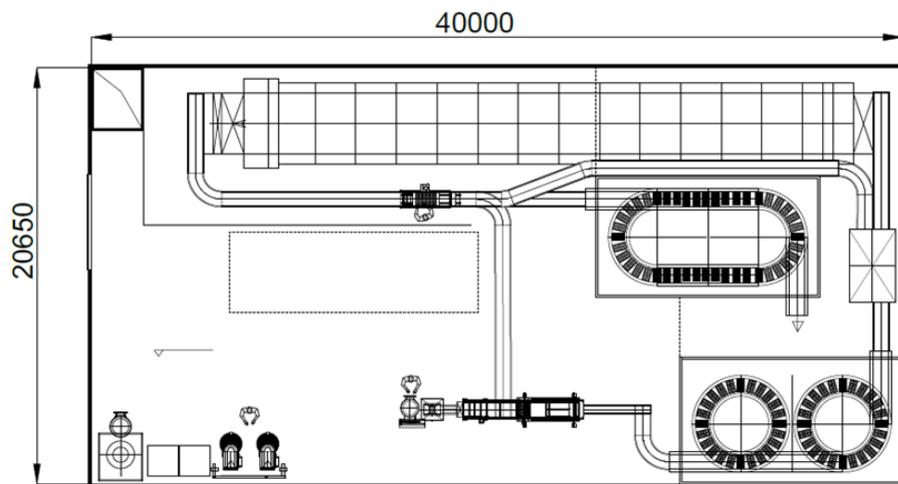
Layout depósito externo con línea de producción. Primera planta. Fuente: Elaboración propia.
